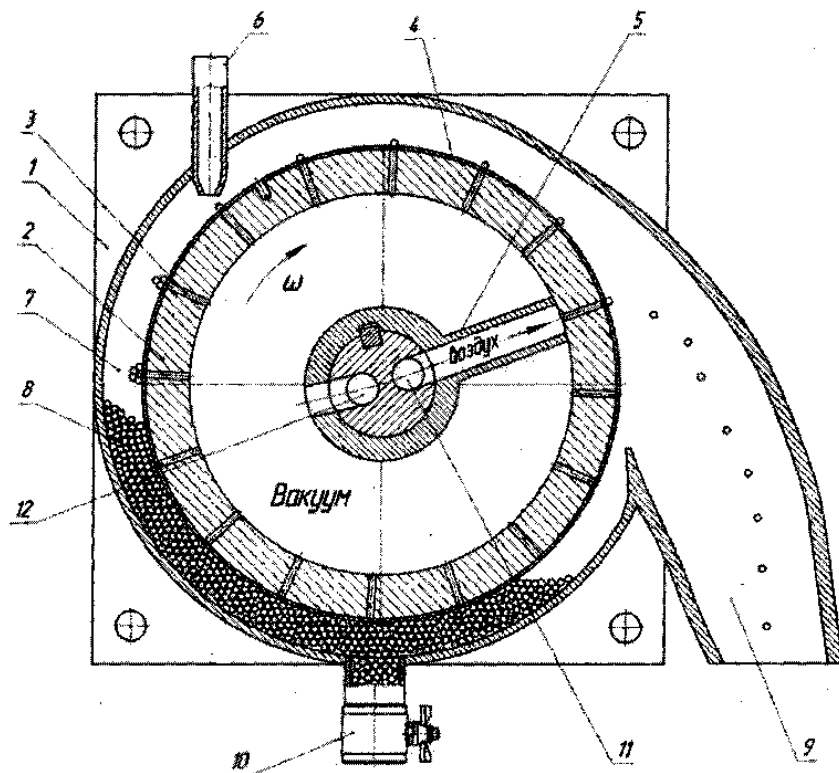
Схема барабанного пневматического высевающего аппарата:
